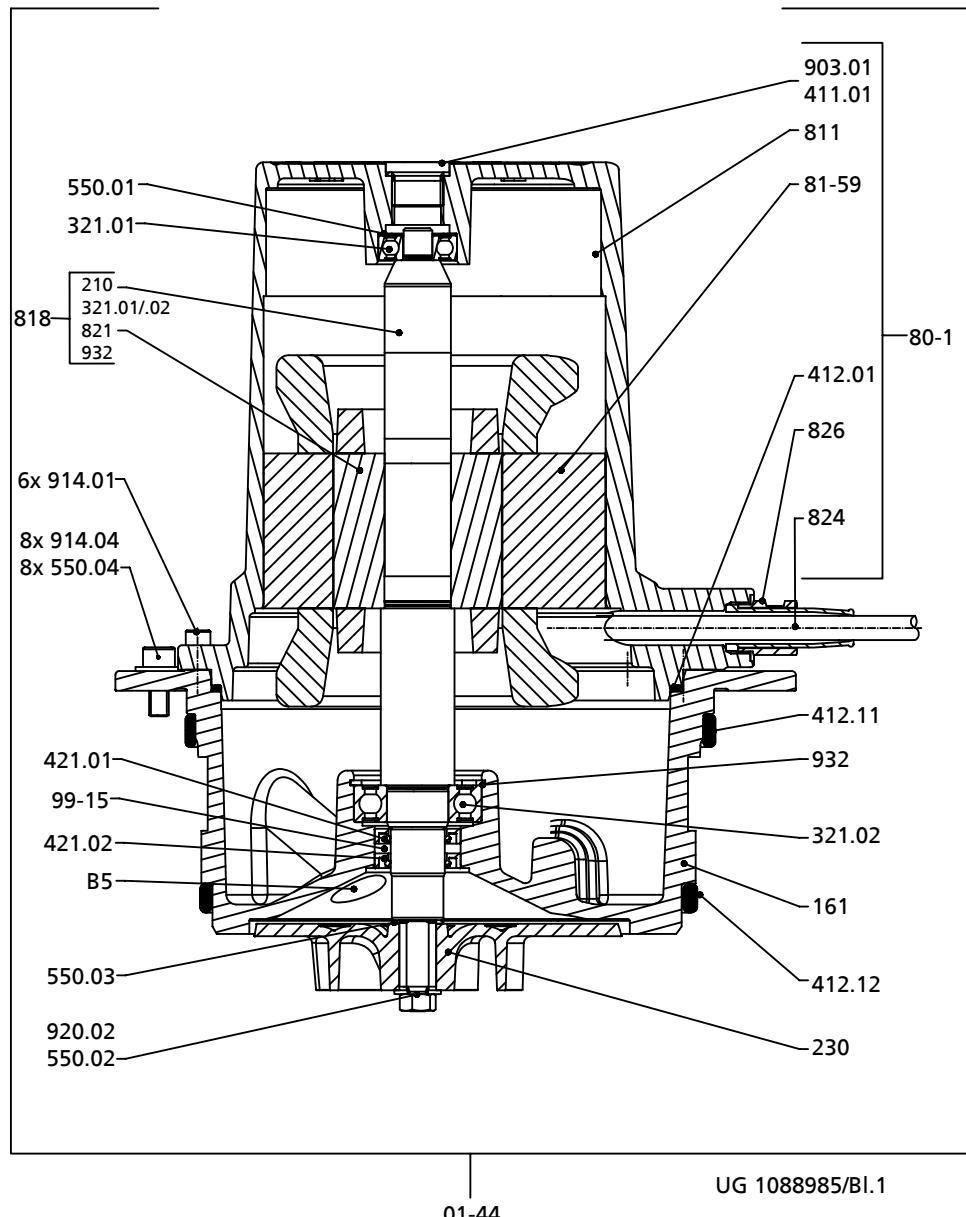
Gesamtzeichnung mini-Compacta U60, U100, UZ150 - Laufteil
